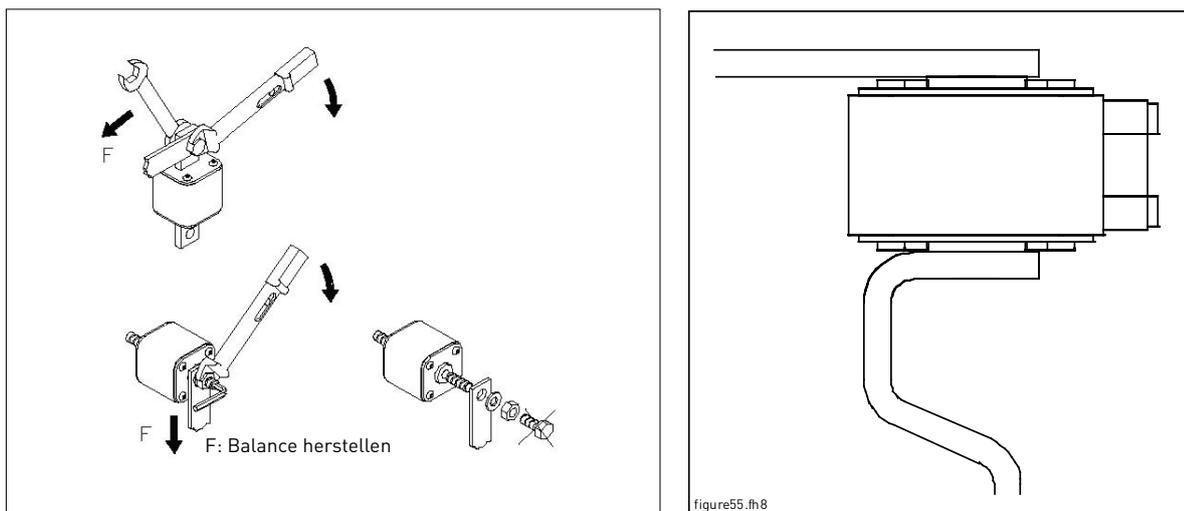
Einbau einer Sicherungen mit Gewindeanschluss (Flush End) – der Anschluss über Sammelschiene wird empfohlen (rechts)
